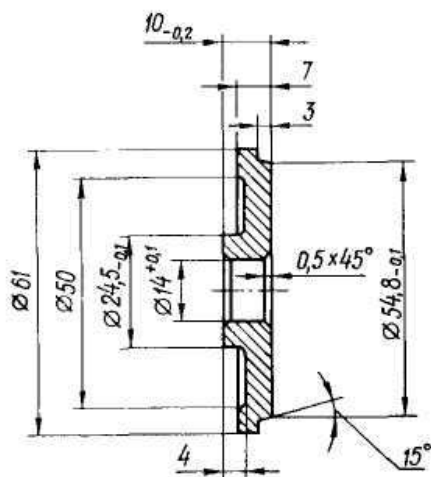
Оправка для запрессовки внутренних подшипников колёсного редуктора
